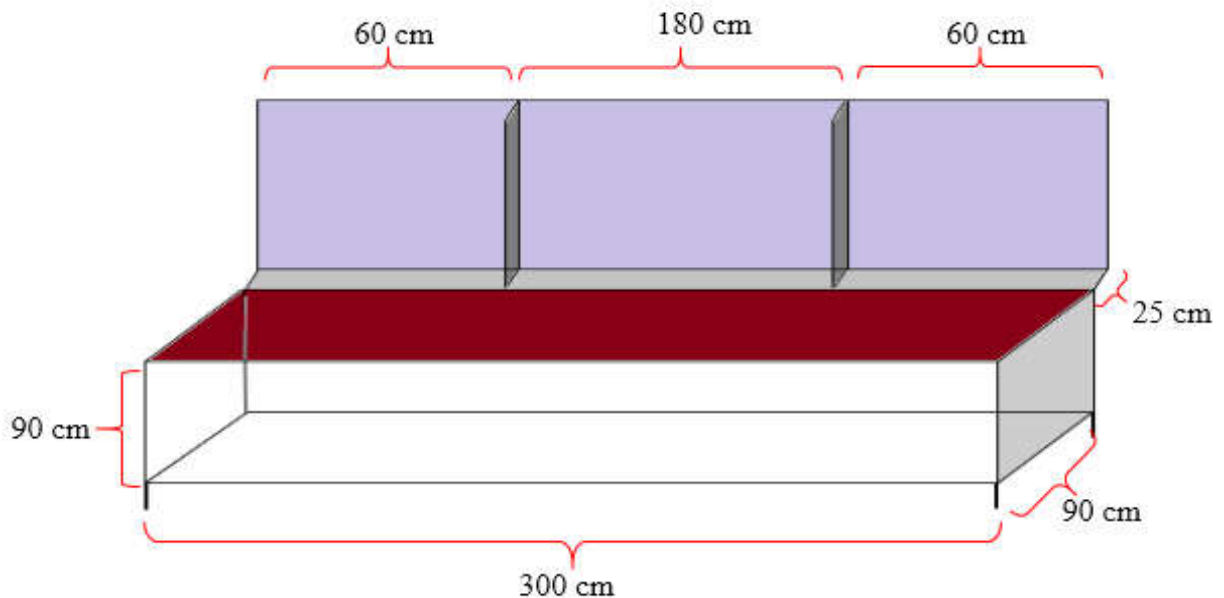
Dimensionnement de la table de stockage des en-cours.
